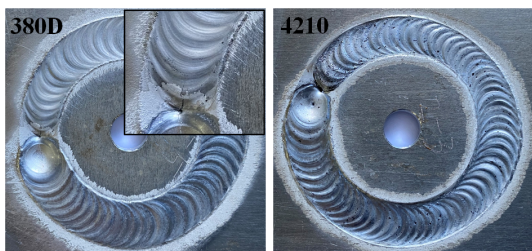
BJ-380D及BJ-4210焊丝抗裂试验
